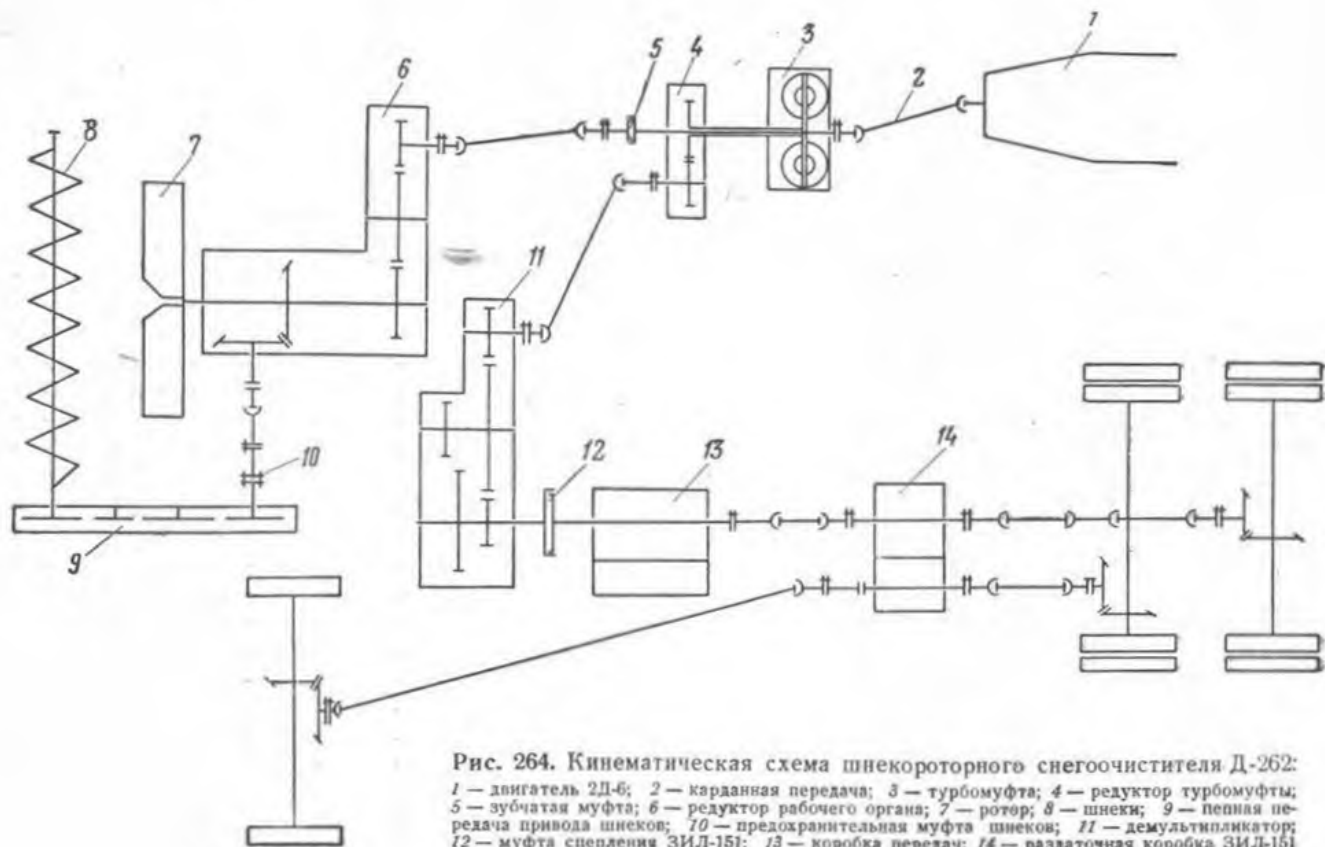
Кинематическая схема шнекороторного снегоочистителя Д-262:
